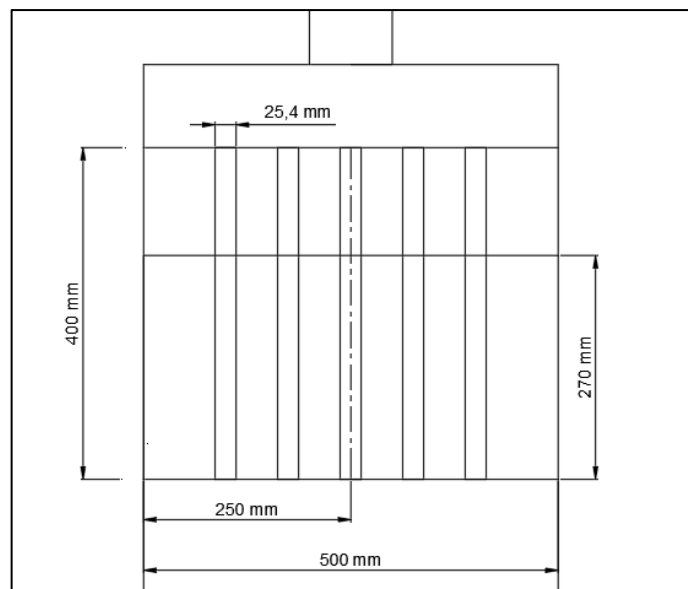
Dimensiones de cámara de agua del caldero
